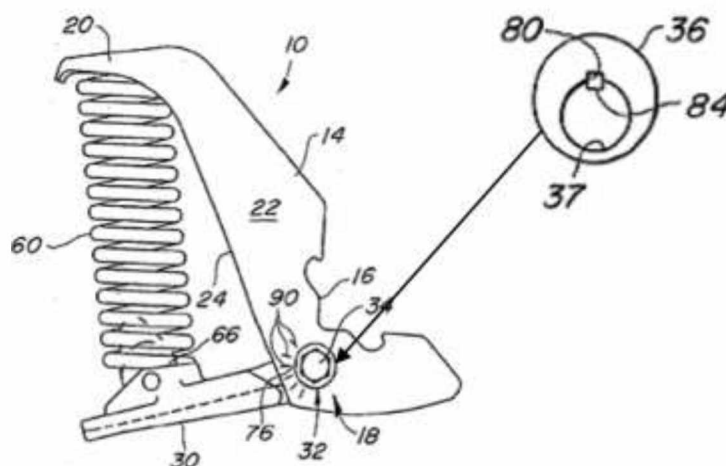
Ексцентриковий механізм навантаження пружини культиватора John Deer
